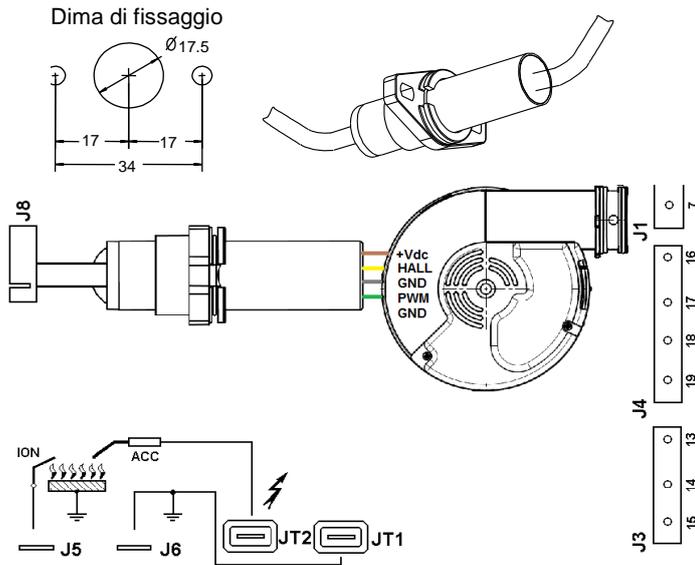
b – Fissaggio e collegamento dell'adattatore motore.
